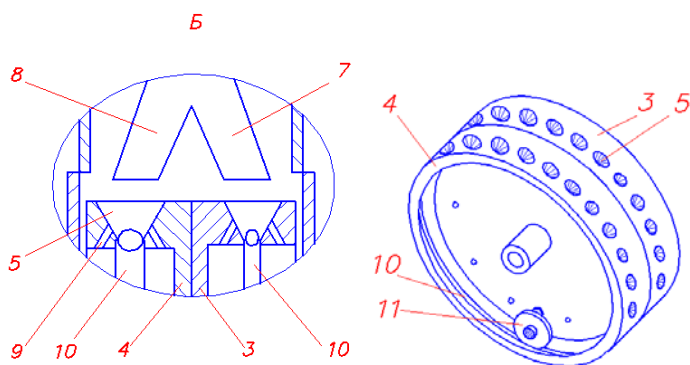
Пневматический высевательный аппарат для совмещенного посева:
